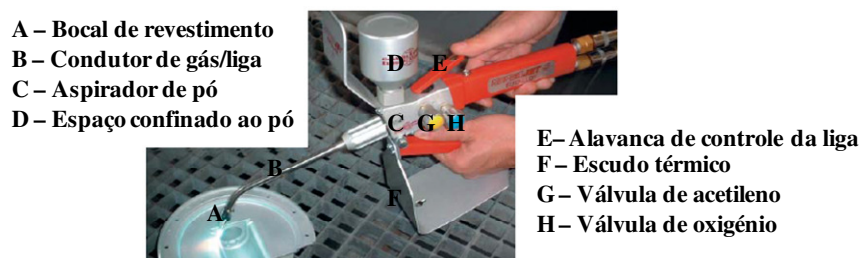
Esquema básico de um equipamento utilizado na deposição manual de revestimentos “Rototec”
